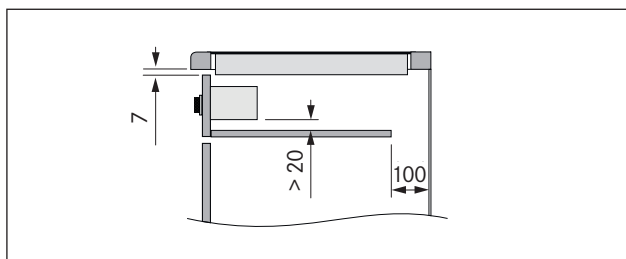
Vista laterale piano di protezione cavi e aerazione
